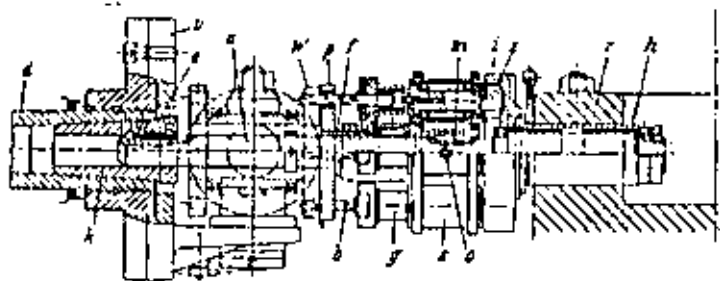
Dispositivo de taladrado de varios husillos para tornos revólver: *a*, husillo de accionamiento; *b*, broca espiral; *c*, lengüeta deslizante; *d*, husillo de torneado; *f*, resorte de compresión; *g*, caja de cabezal taladrador; *h*, soporte; *i*, corona de dientes interiores; *k*, cono conductor; *m*, lengüeta ajustada; *o*, prisionero; *p*, placa de guía de brocas; *r*, eje del revólver; *s*, husillos de taladrado; *u*, dispositivo de sujeción; *v*, ruedas de dientes rectos; *W*, pieza.
